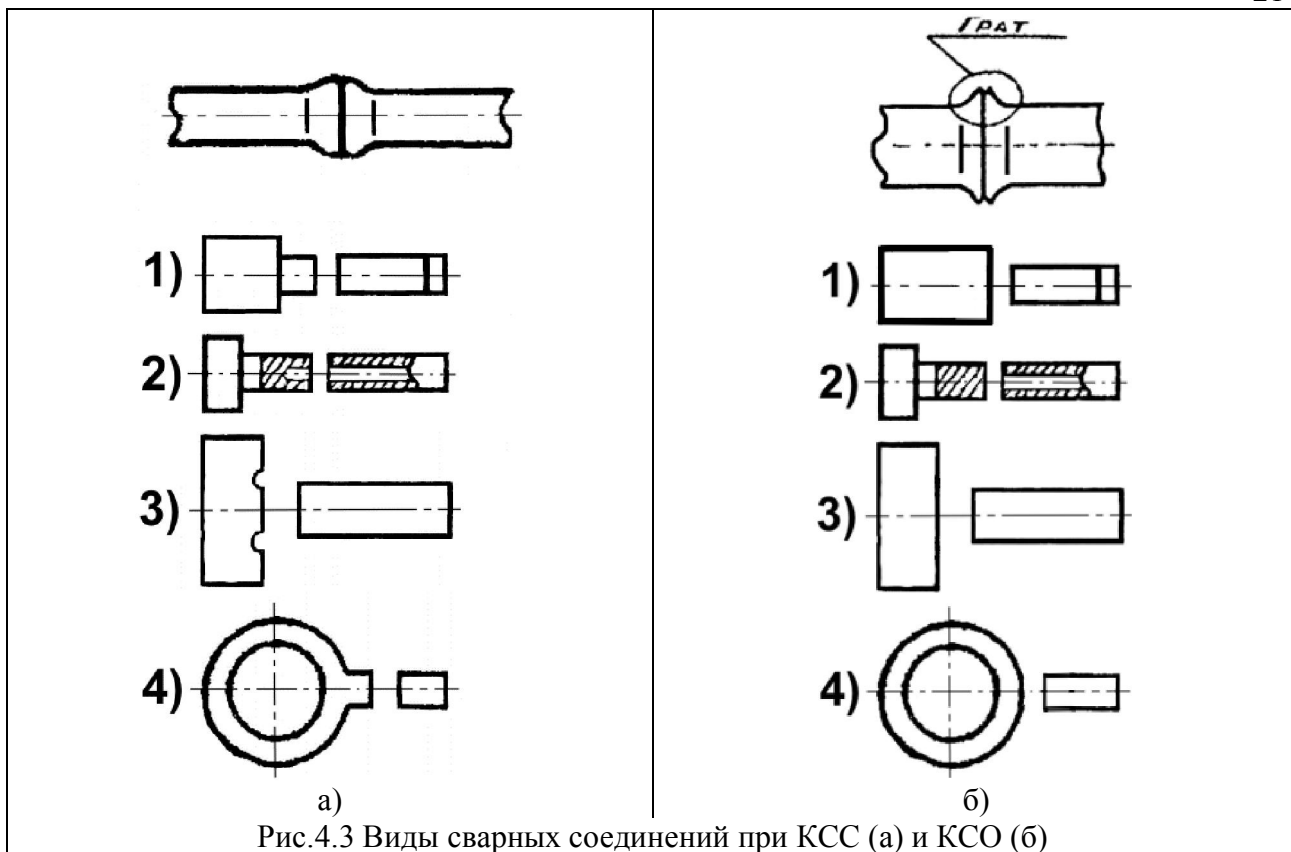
Виды сварных соединений при КСС (а) и КСО (б)
